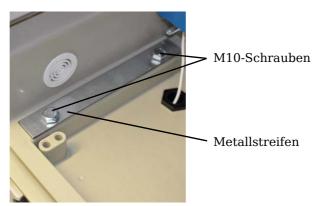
Verbindung DCB - Sockel (Ansicht linke Seite DCB innen)
